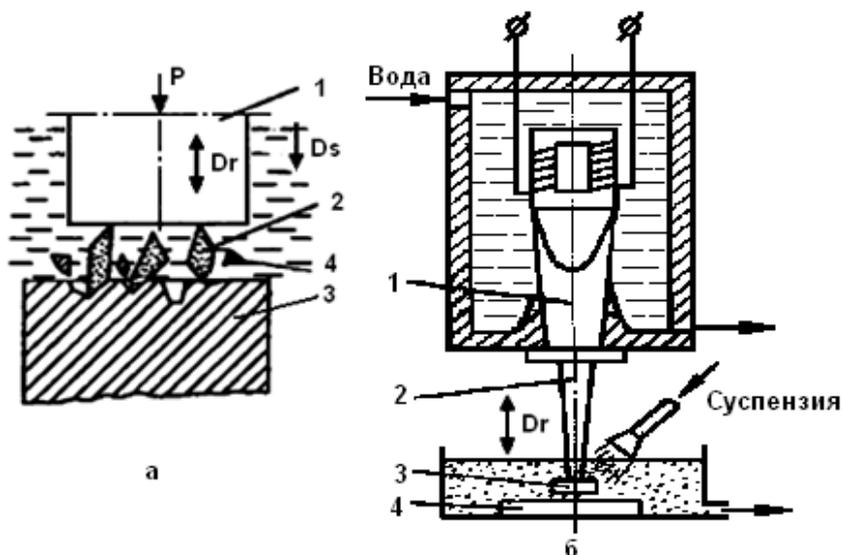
Ультразвуковая обработка: а – схема разрушения обрабатываемого материала; б – схема ультразвукового станка
